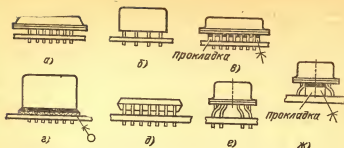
Варианты установки различных корпусов на печатную плату с металлизированными отверстиями
